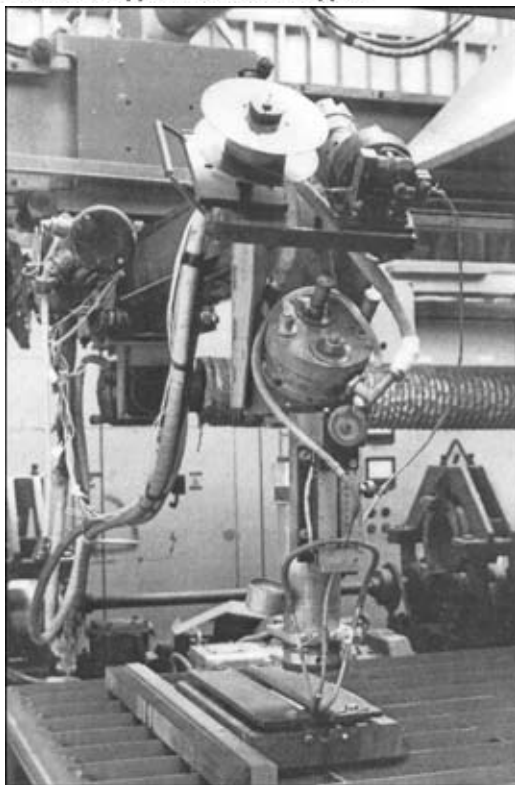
Общий вид сварочной головки для лазерной сварки с подачей присадочной проволоки
